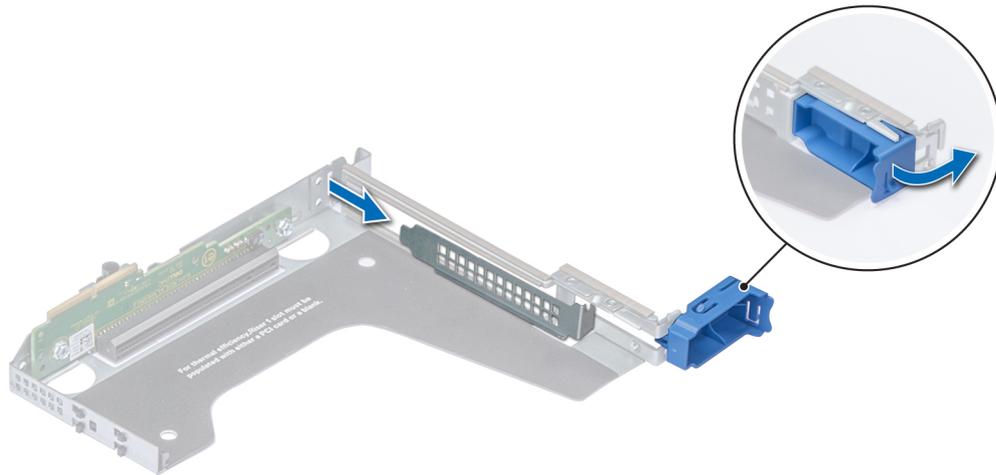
Retrait d'un support de plaque de recouvrement pour la carte de montage 1
